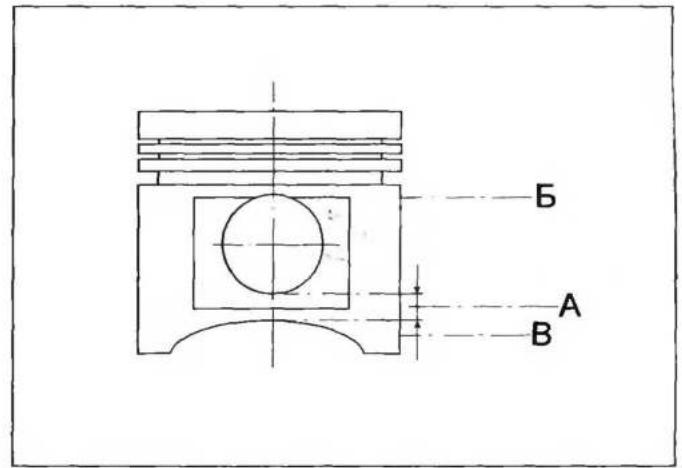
Пояс для измерения размера юбки поршней различных конструкций:
